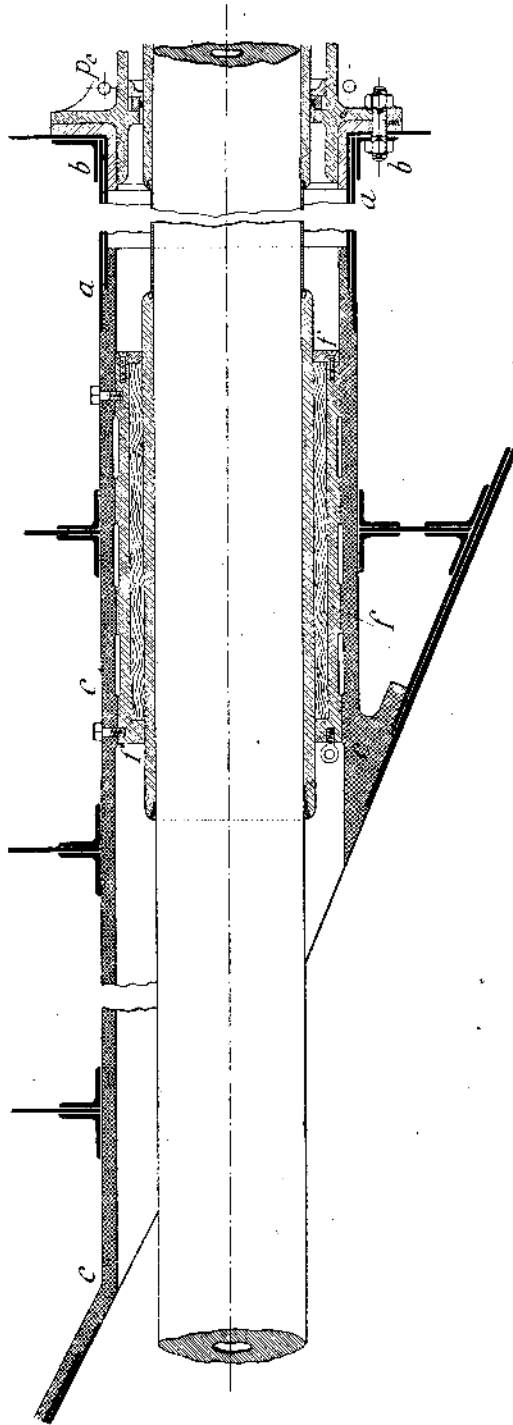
Tube de coque (mêmes détails que pour le tube d'étambot).
